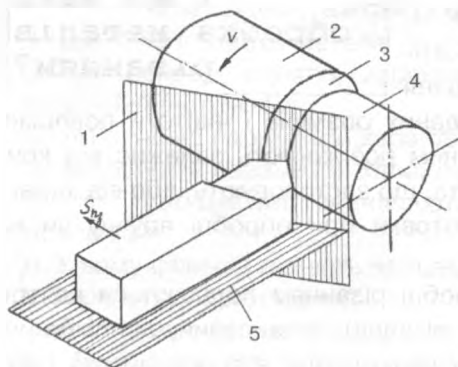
Координатні площини і поверхні оброблюваної заготовки
